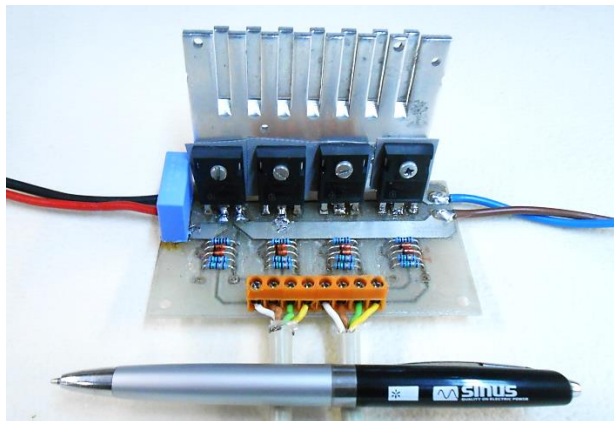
PCB desenvolvida para o conversor CC-CA.
